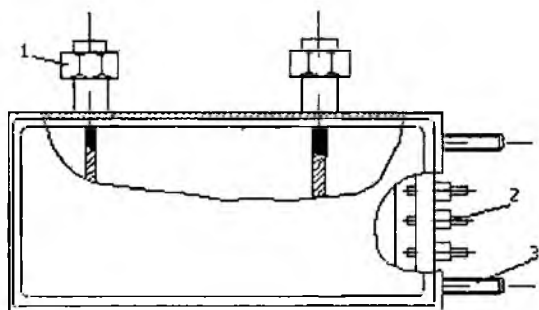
Конструкторсько-технологічний варіант виконання мікроблоку з комбінованим фрезерувально-штамповочним корпусом:
